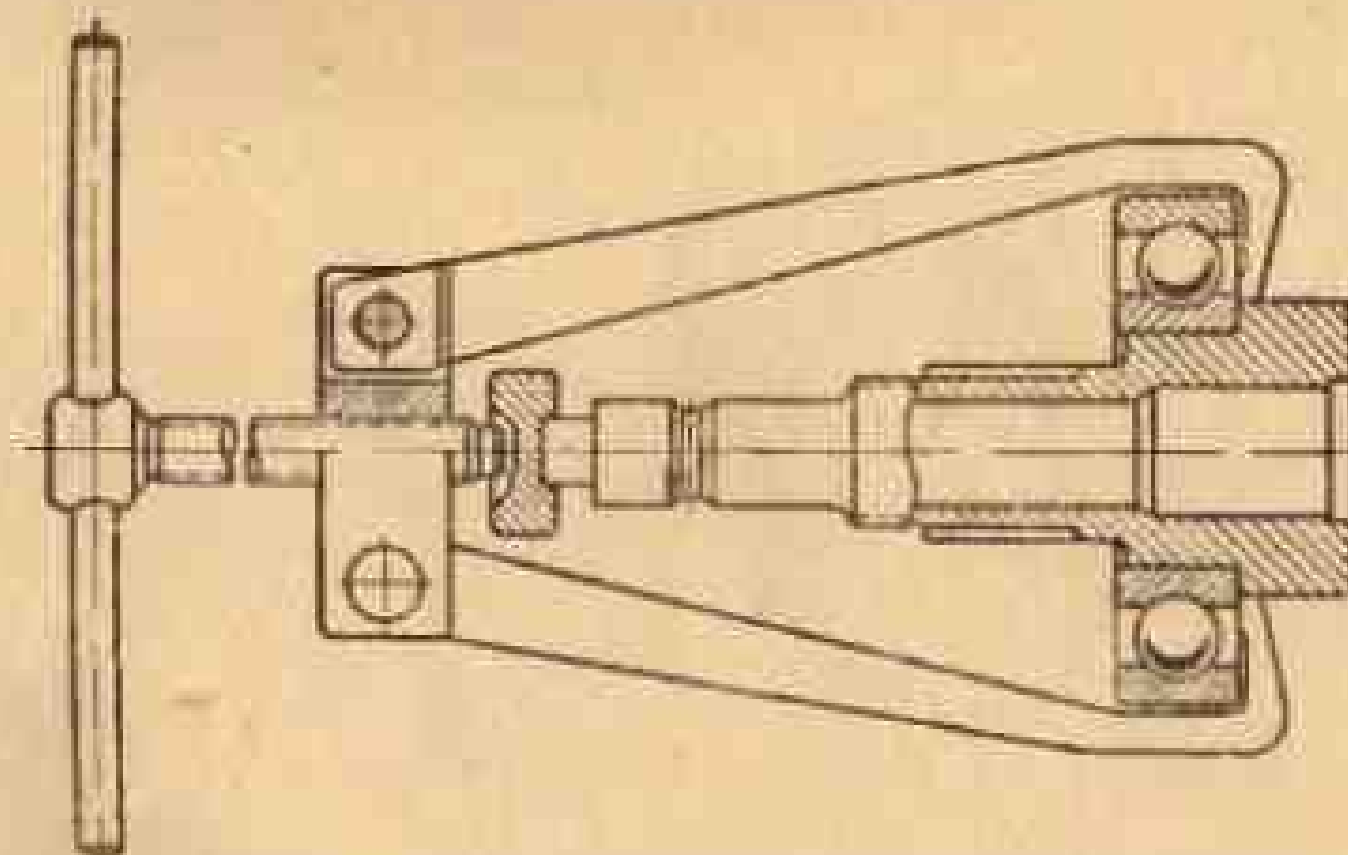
Съёмник для снятия вала шаткоподшипника и шестерён в 40 и 32 зуба
